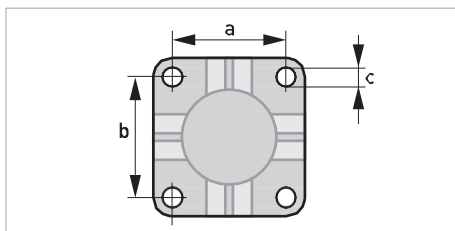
Розміри монтажної пластини корпусу польового виконання
